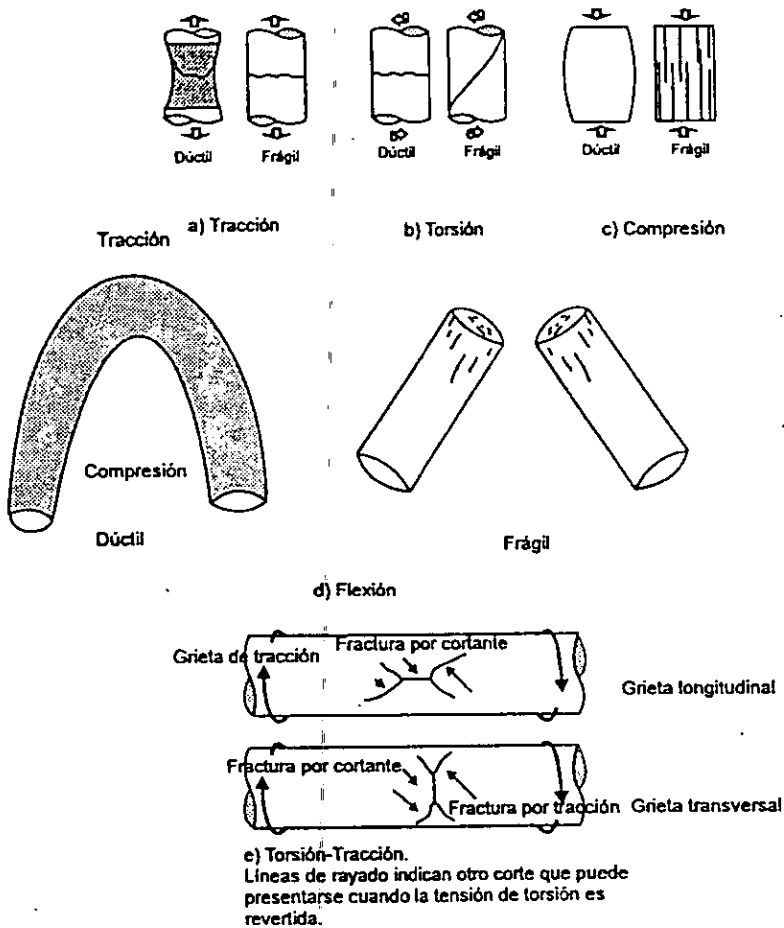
La apariencia de las fisuras bajo diversas orientaciones de esfuerzos..
